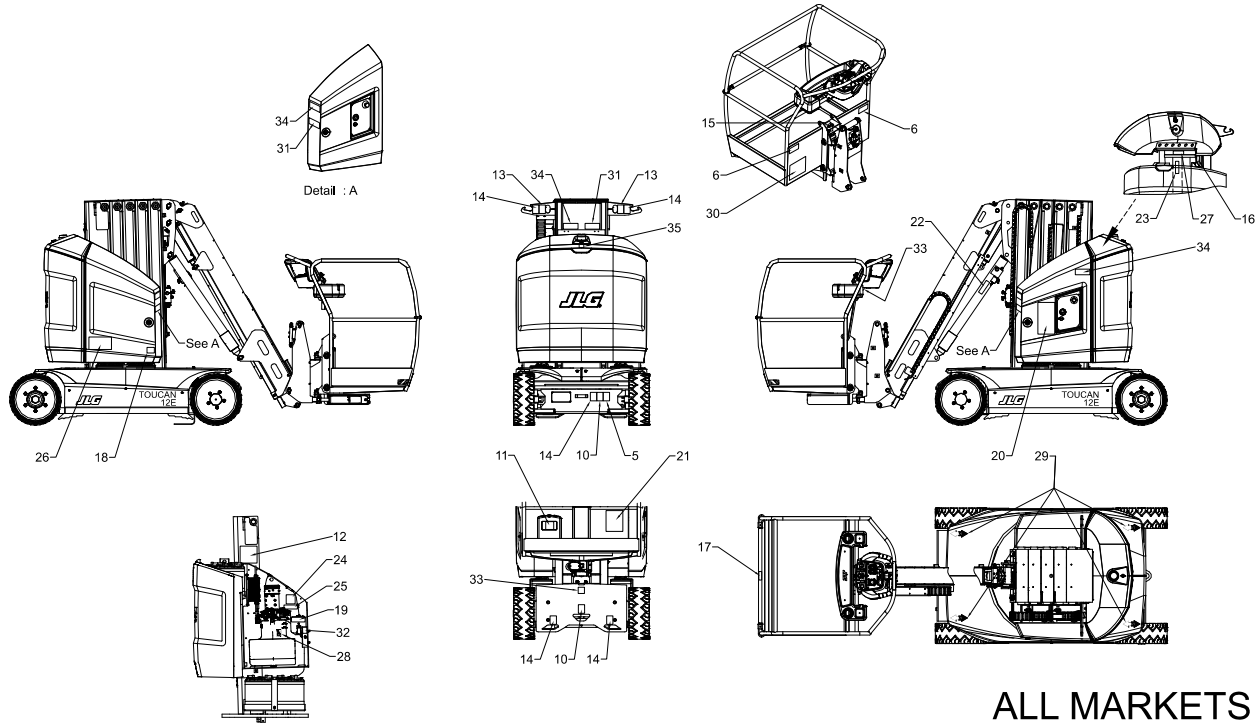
Anbringung der Maschinenaufkleber - Blatt 1
